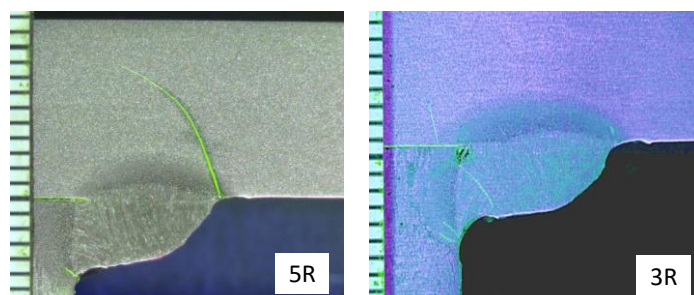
き裂導入後 UIT 施工試験体の断面観察
